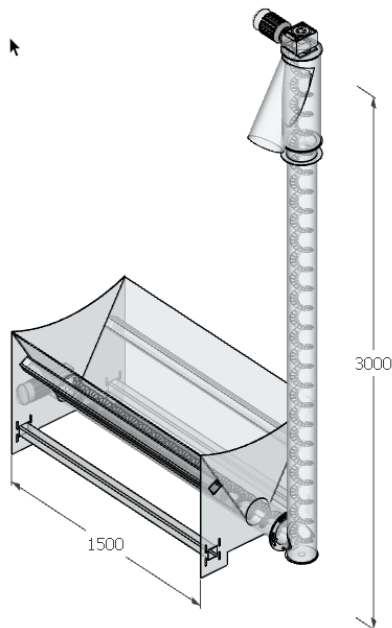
Prinzipschema des Holzhackschnittel-Transportsystems zur Befüllung des Schubbodencontainers und als Messstrecke
